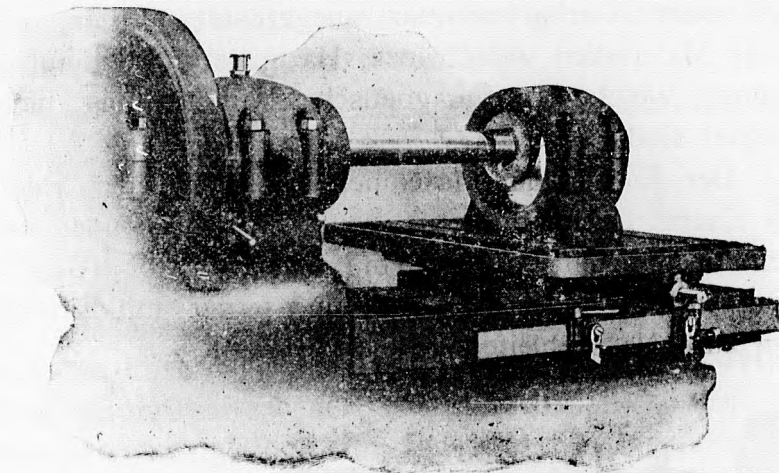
Z. A.: Zwei neue Special-Schleifmaschinen.
